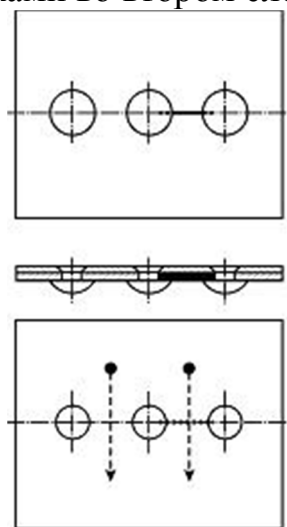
Стандартный образец, имитирующий двухслойное заклепочное соединение с дефектом.
